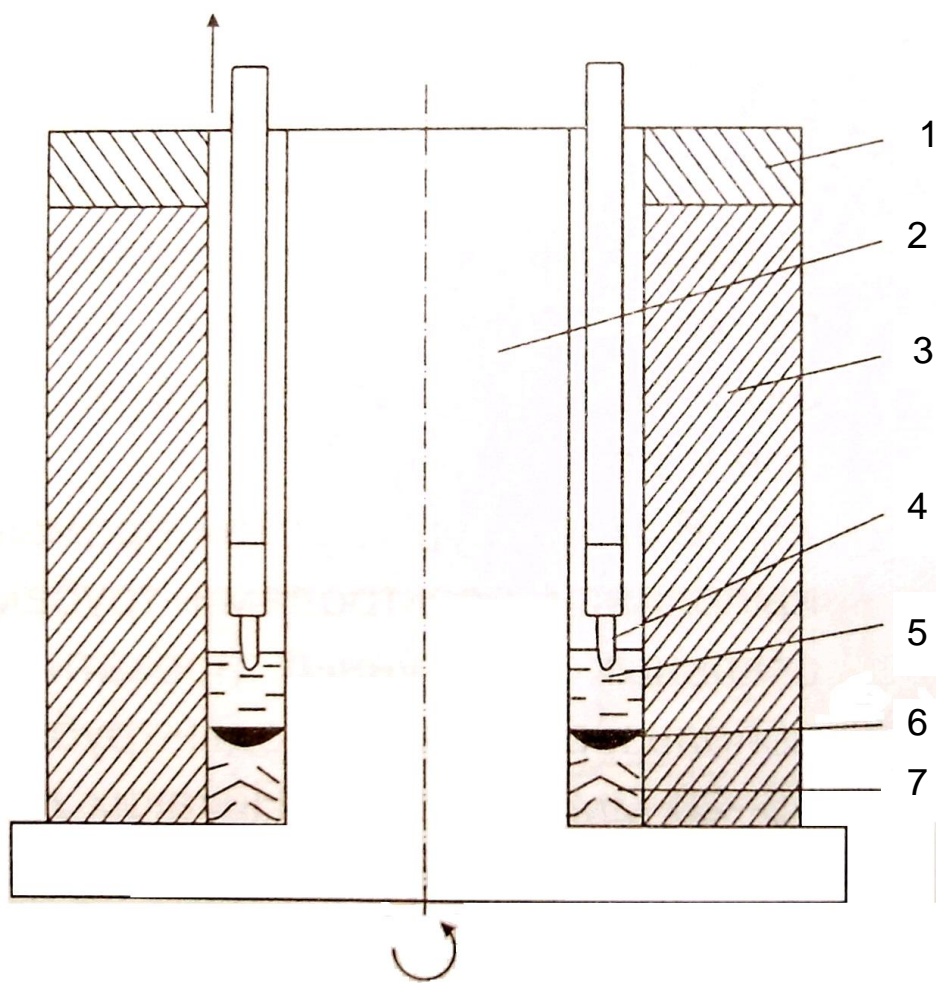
Схема ЭШН внутренней цилиндрической поверхности:
